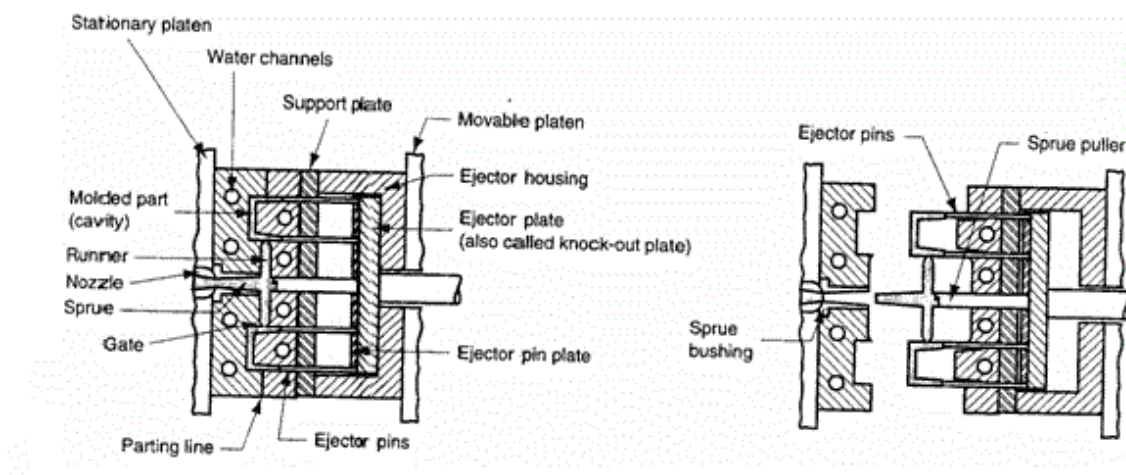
Constituintes de um molde (adaptado de https://www.alibaba.com/product-detail/plastic-injection-moulding-machine-with-price_60061594617.html n.d.).
